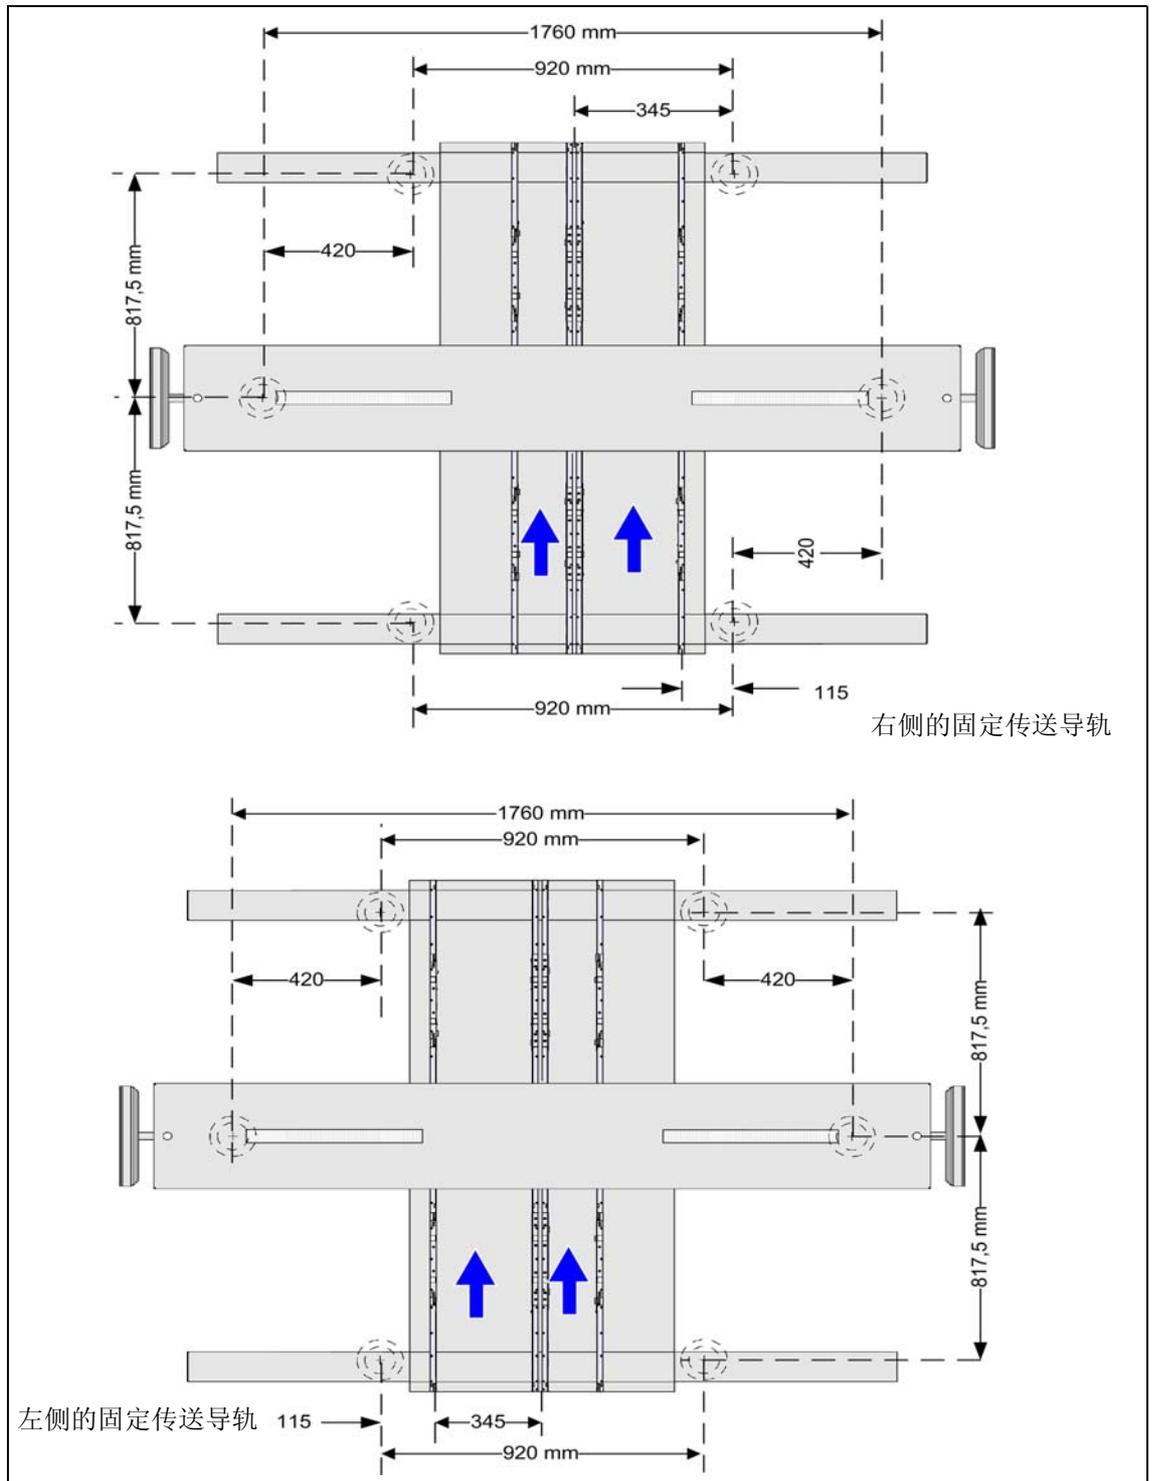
PCB 双传送导轨的贴片机支脚间隙 (单位毫米)
